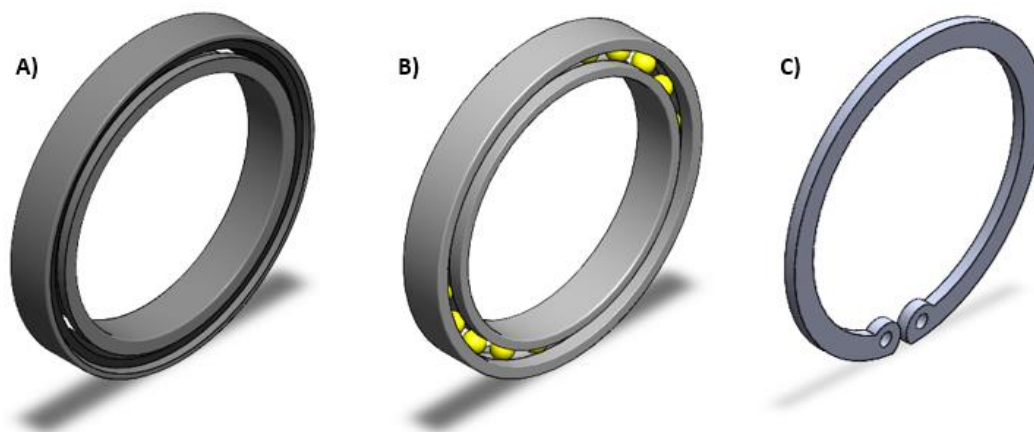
Models CAD de: A) Rodament de contacte angular; B) Rodament radial; C) Circlip
